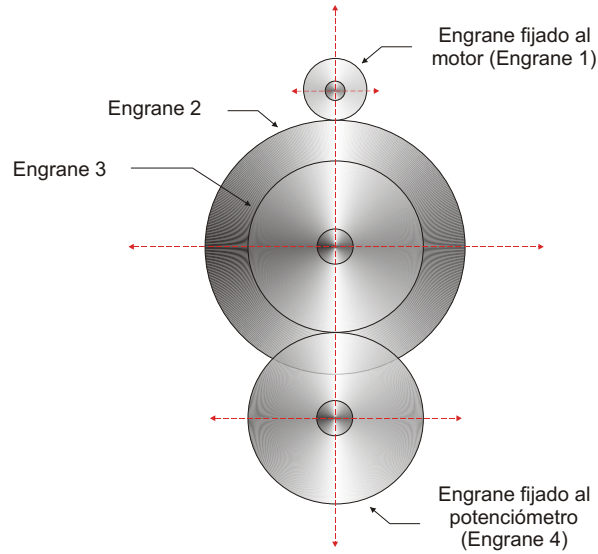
Arreglo de engranes del *sistema acoplamiento*.
